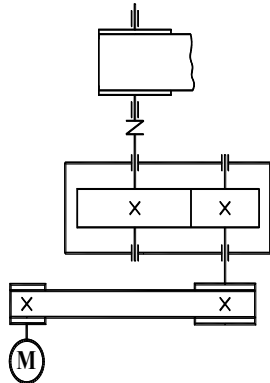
Цилиндрический одноступенчатый редуктор с ременной передачей
